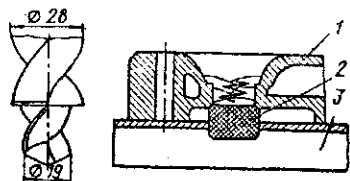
Инструмент для обработки свечного отверстия и схема его заварки (ломаная стрелка показывает последовательность оплавления присадочного прутка):
